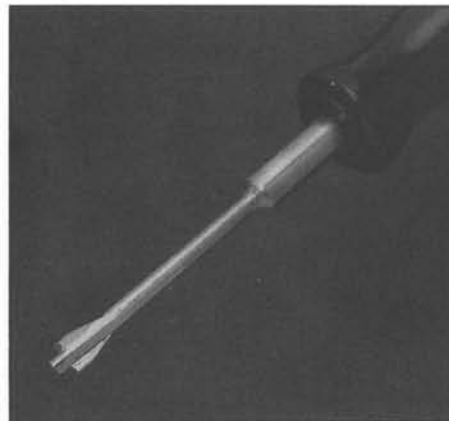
Korrekturwerkzeug für das Tastenlager und ...
